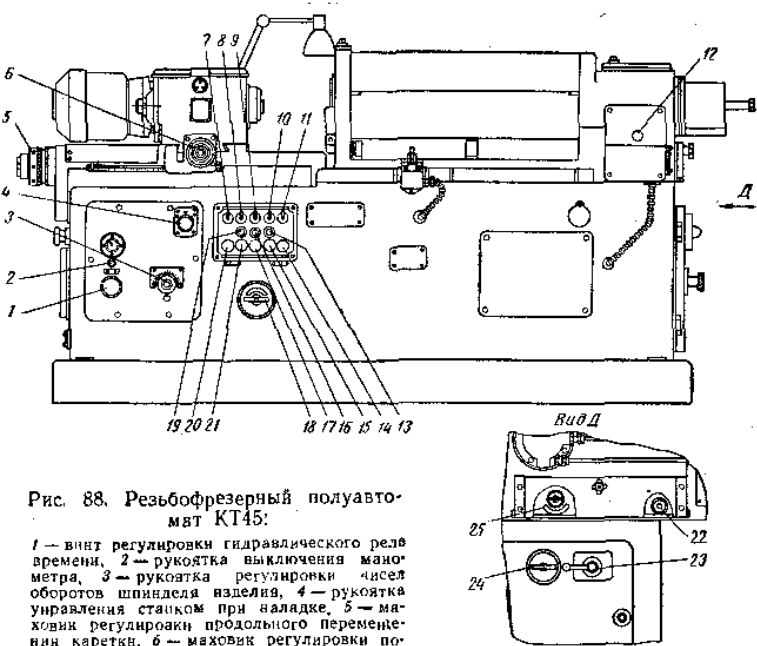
Резьбофрезерный полуавтомат КТ45:
